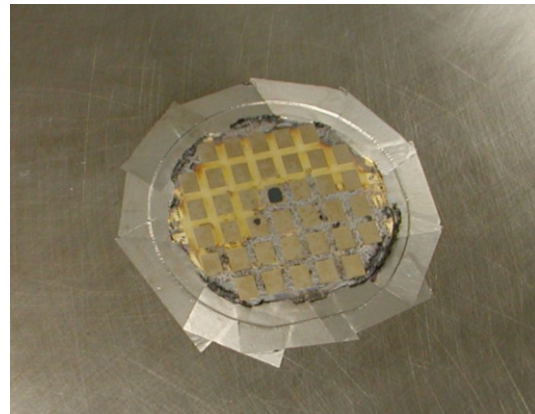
Nickelwerkzeug nach Entfernen des Werkzeugoriginals
